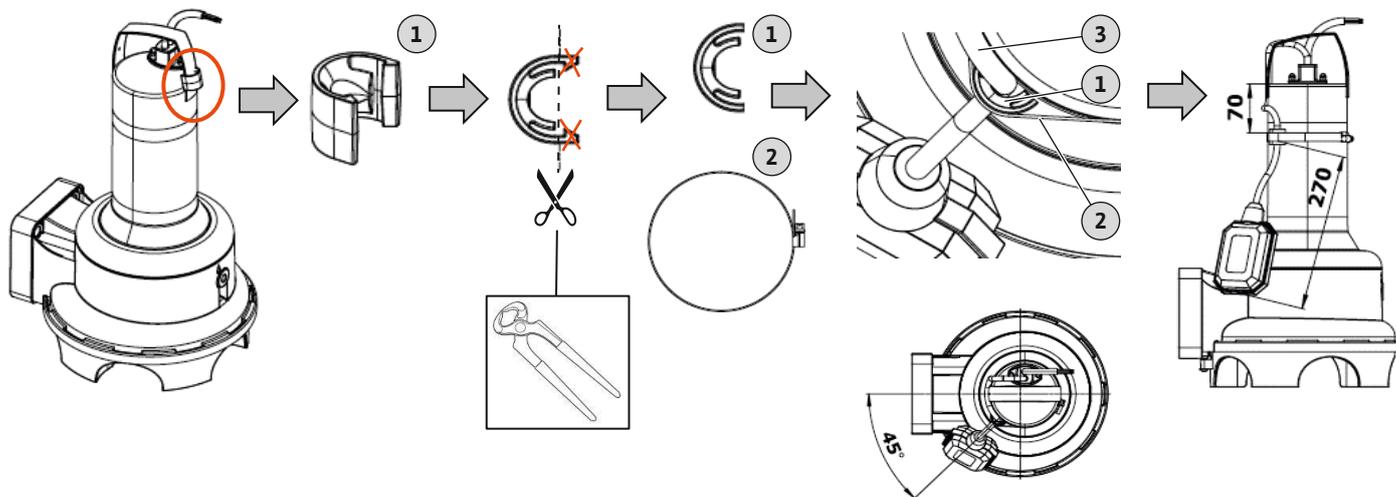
Rеха UNI: длина кабеля поплавкового выключателя
